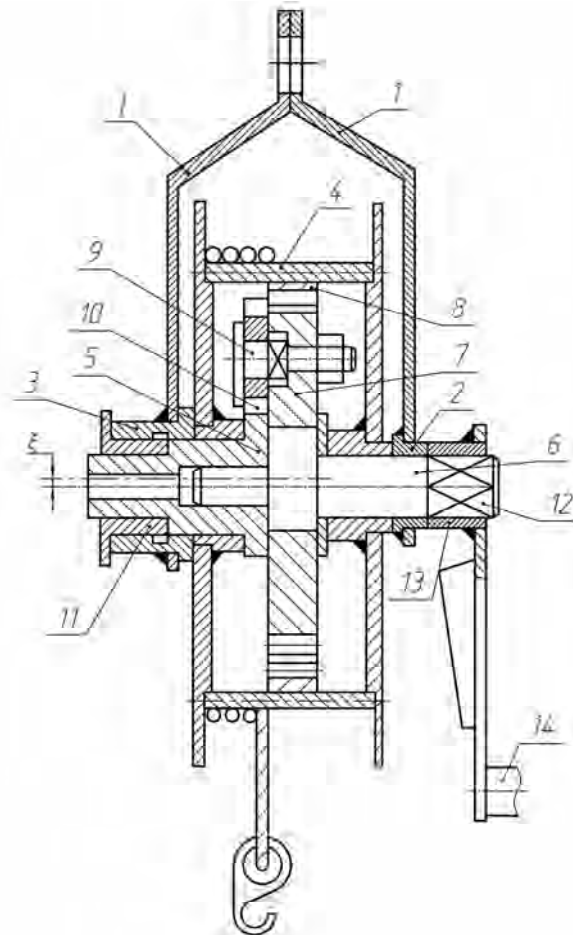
Конструкция лебедки с планетарной зубчатой передачей эксцентрикового типа (патент 1562299)
